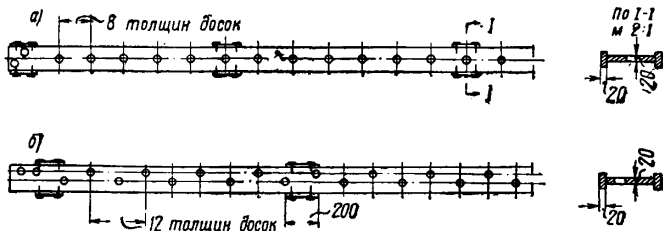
Кондукторы для предварительной забивки гвоздей в полки балок
